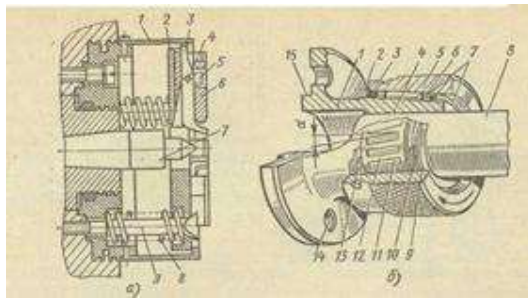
Патроны: а - самозажимный плавающий; б - з роликовым затиском
